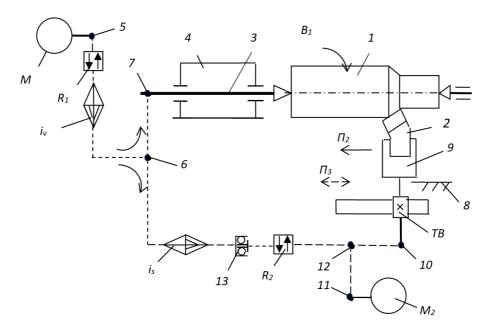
Частная структурная схема станка для обработки цилиндрической поверхности
